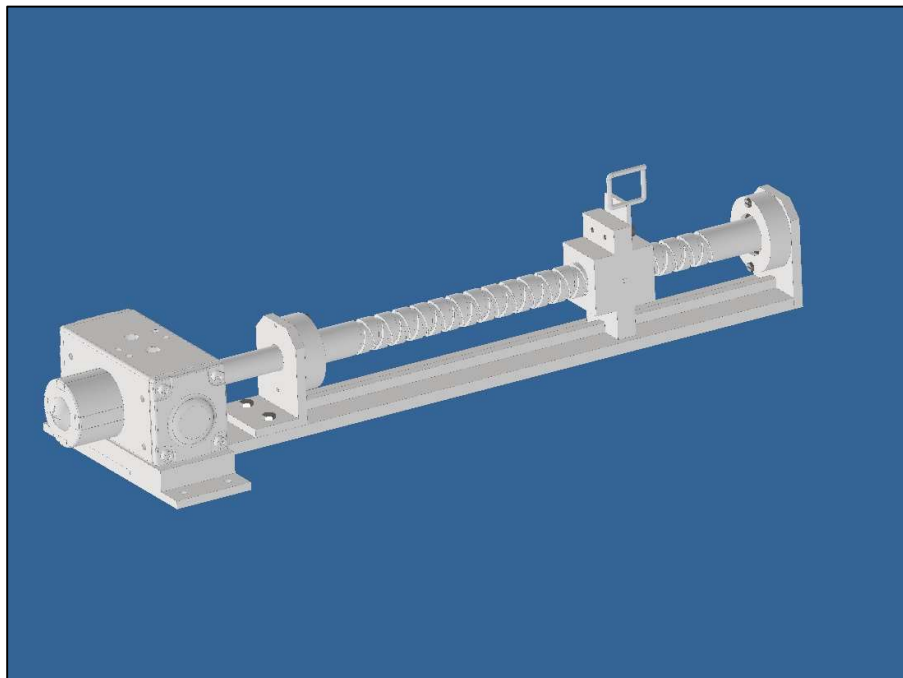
Platzierung der Dichtung mit einer Gewindestange
